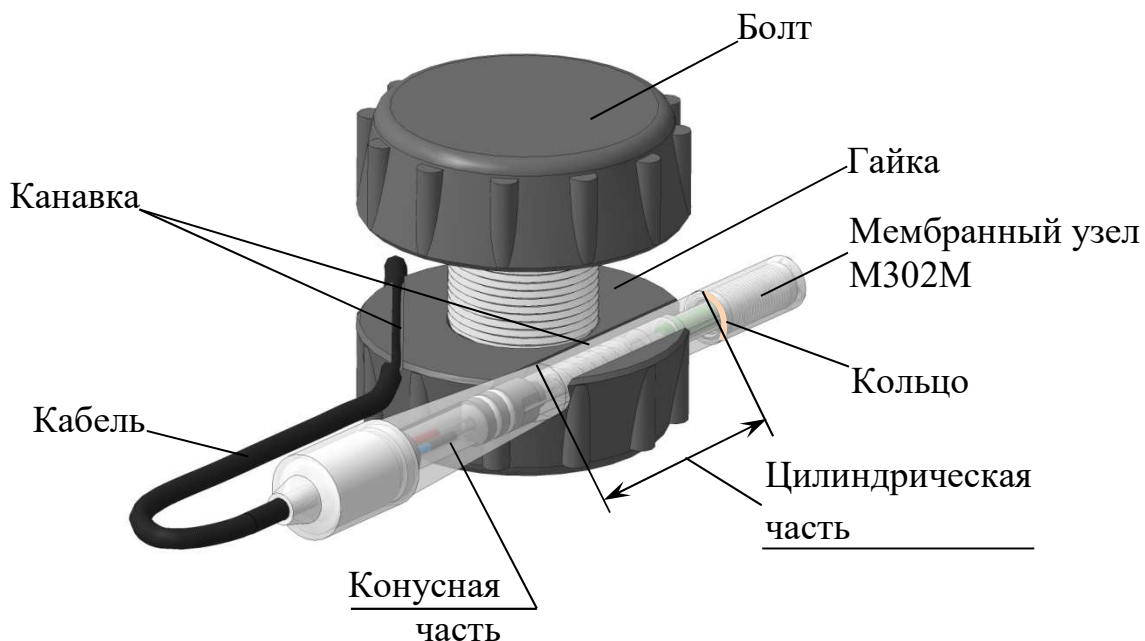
Расположение датчика кислородного ДК-302 в корпусе насадки
